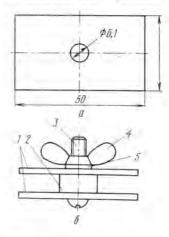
1 — щечка [дюралюминий толщиной 1...2 мм], 2 шт.; 2 — бобышка; 3 — винт M6×20; 4 — барашек [гайка] M6; 5 — шайба
